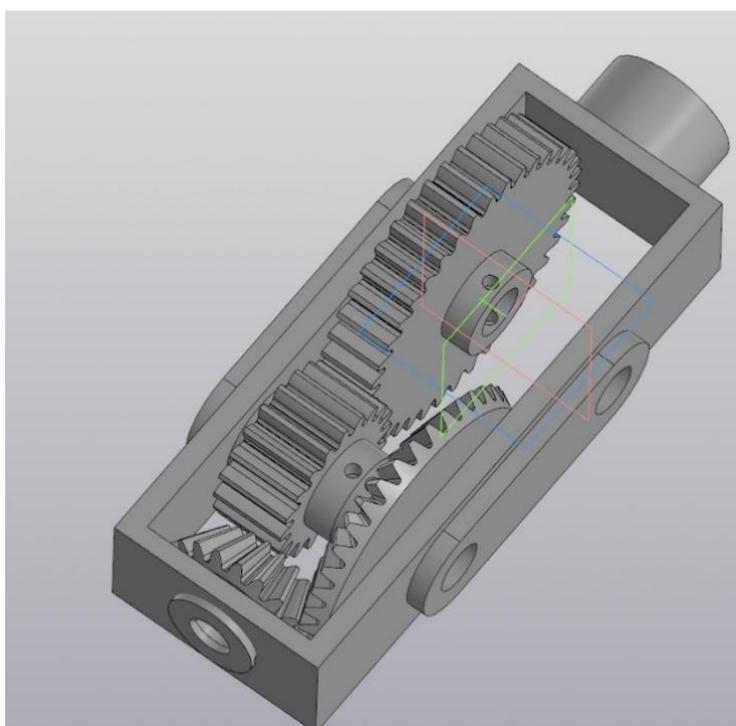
Предварительная 3D-модель зубчатой передачи в корпусе.
